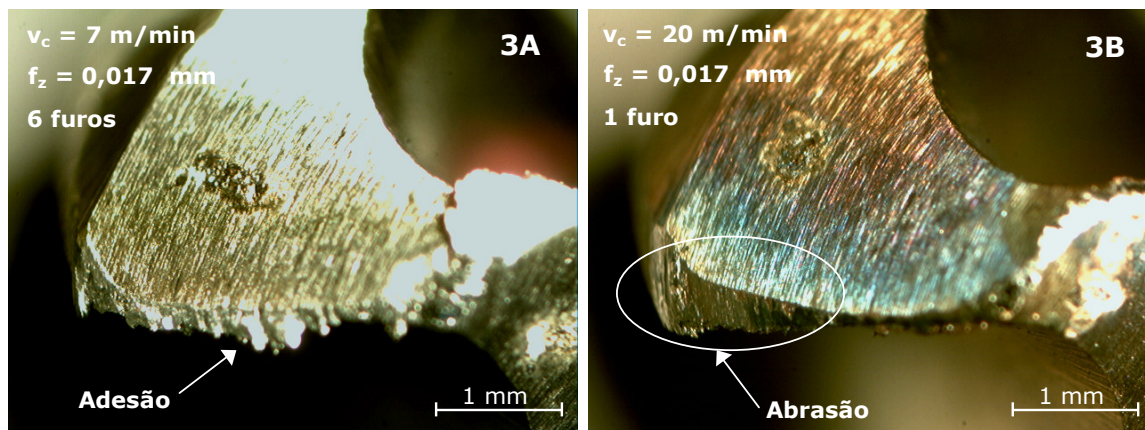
Desgaste de flanco da ferramenta na usinagem com diferentes parâmetros de corte.
